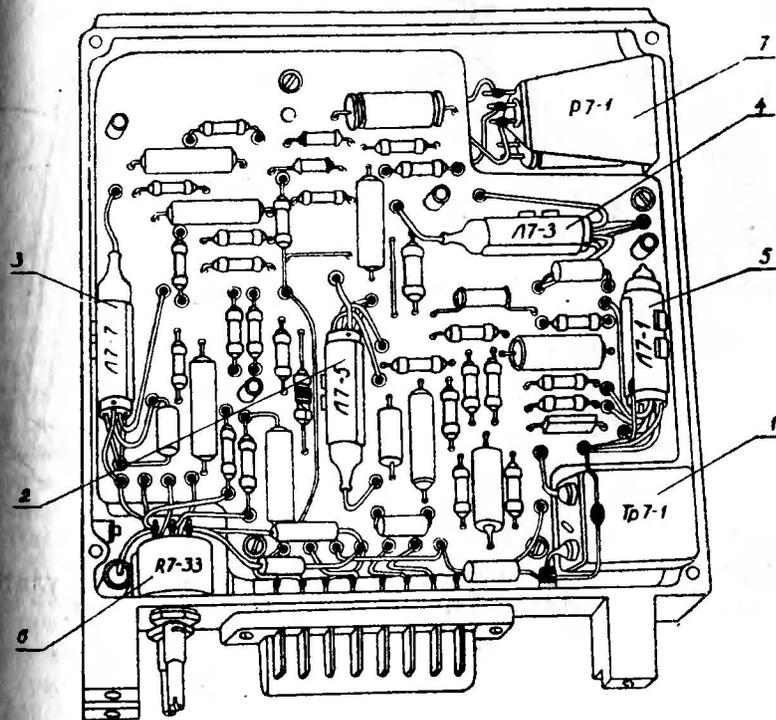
Расположение деталей и монтажа блока подмодулятора и дуплексного устройства — блока № 7 (вид сверху).
